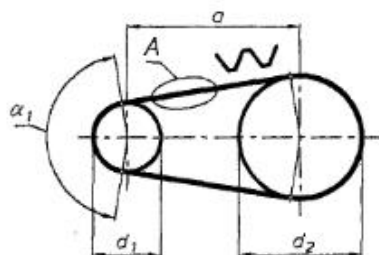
Схема и основные размеры зубчато-ременной передачи
